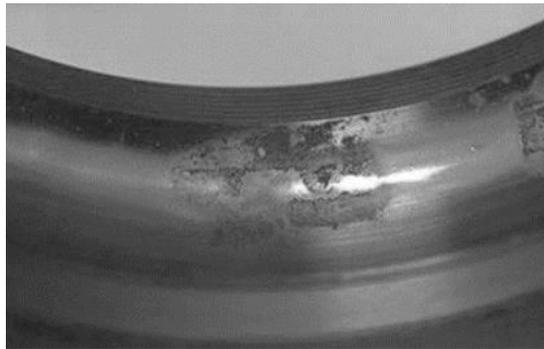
Défaut de roulement – corrosion. [15]
